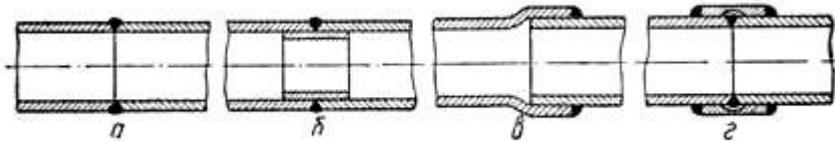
Типы сварных соединений труб: *a* — стыковое; *б* — с вкладышем; *в* — встраструб; *г* — стыковое с вкладками
